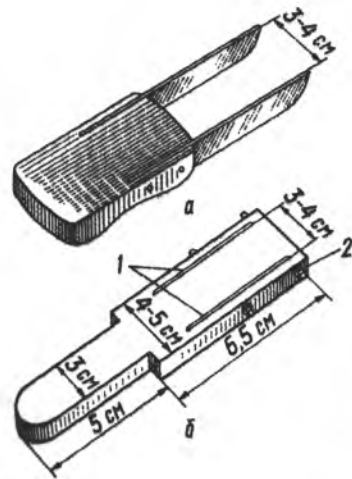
Ножі нової конструкції для зрізування трубки і підготовки підщепи до окулірування трубкою (дудкою):
